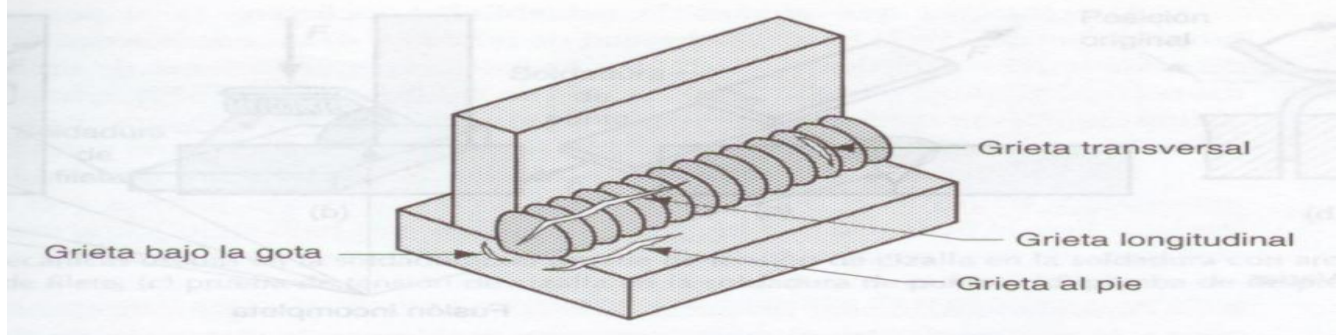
Diferentes formas de cuarteaduras en una soldadura.
